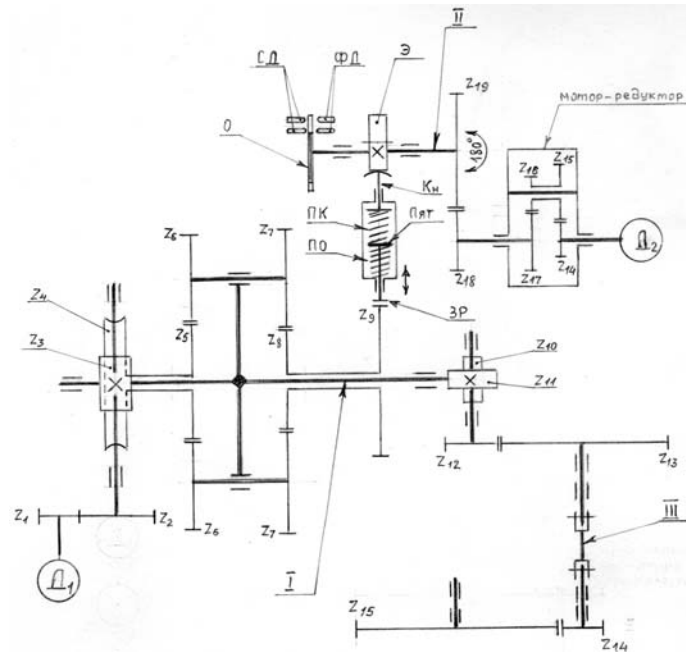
Кинематическая схема привода установочного поворота оси склонений.
